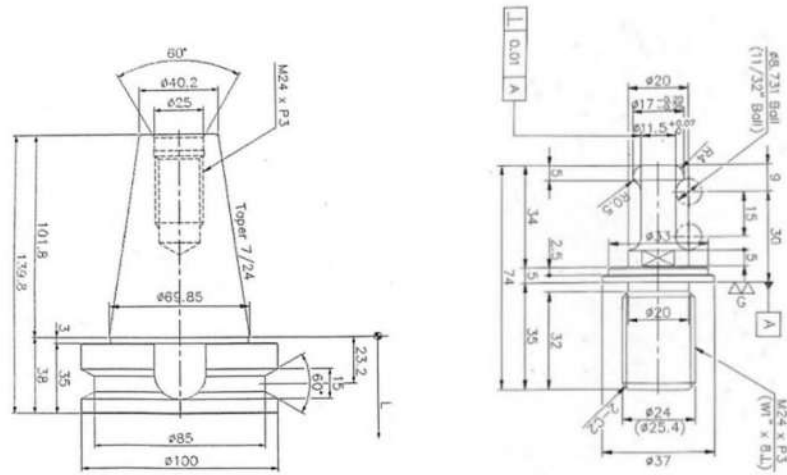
Креслення фрезерної оправки DIN 69871
